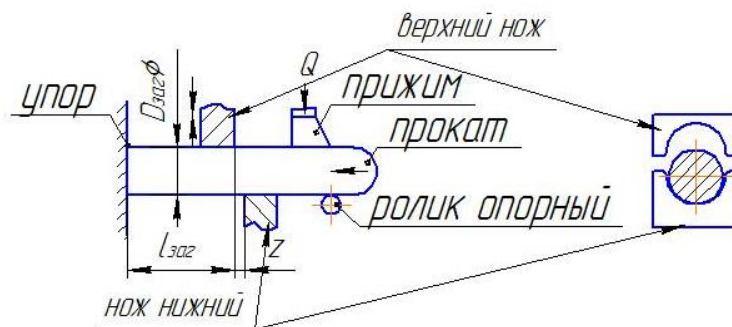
Кинематическая схема пресс-ножниц
